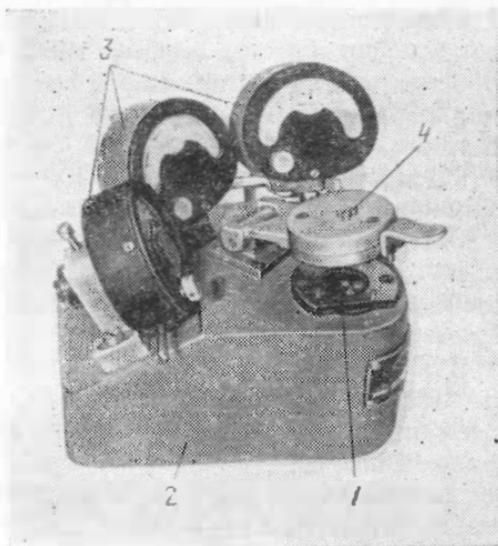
Прибор для проверки осевого зазора промежуточного, секундного и анкерного колес:
